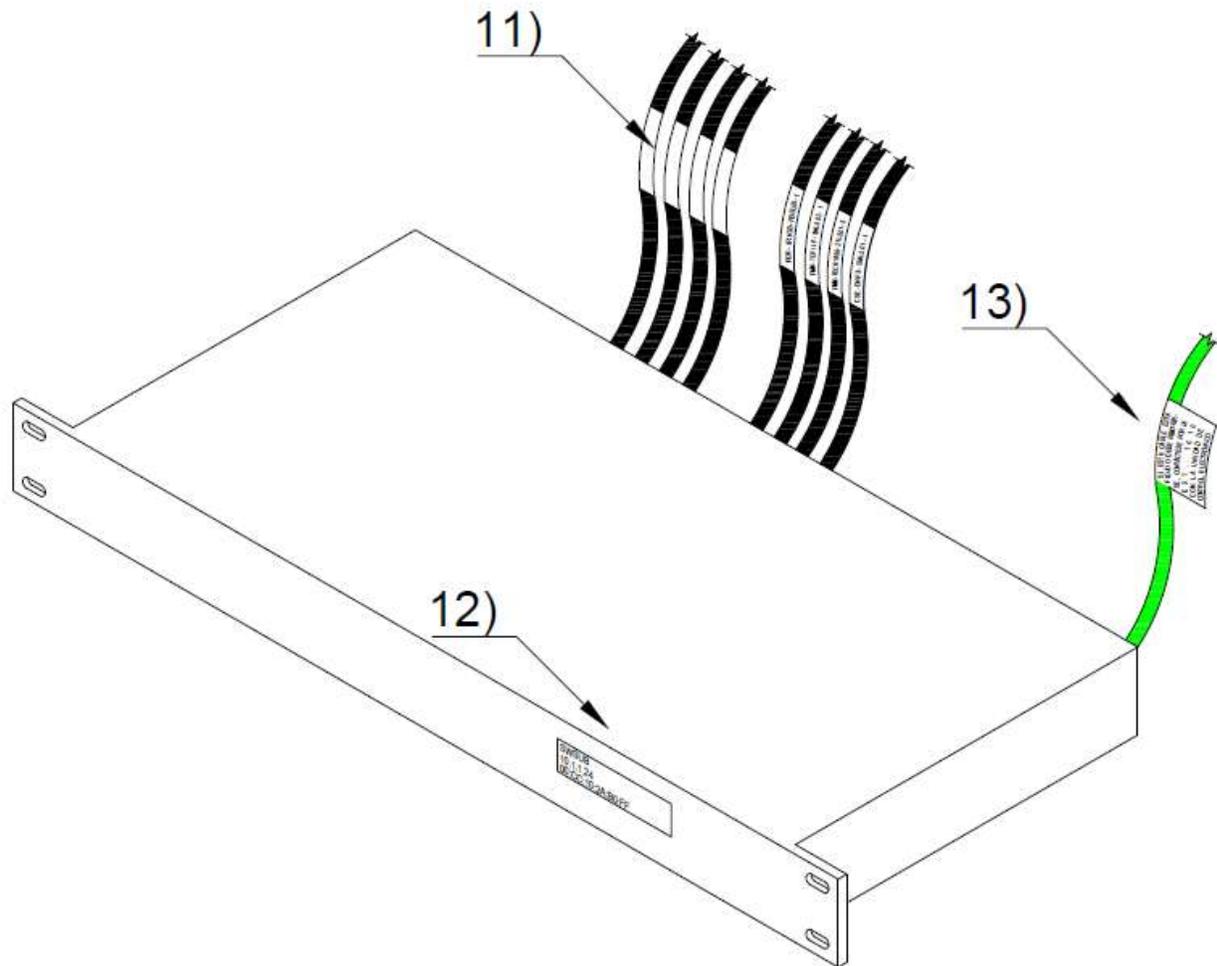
Etiquetas de cableado estructurado, puestas a lo largo del conductor: Etiqueta de dispositivo para cableado de aterrizajes según ANSI-J-STD-607A.
